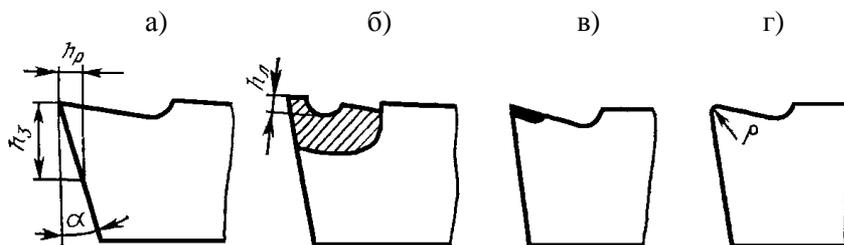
Геометрические формы износа режущего лезвия токарного резца:
